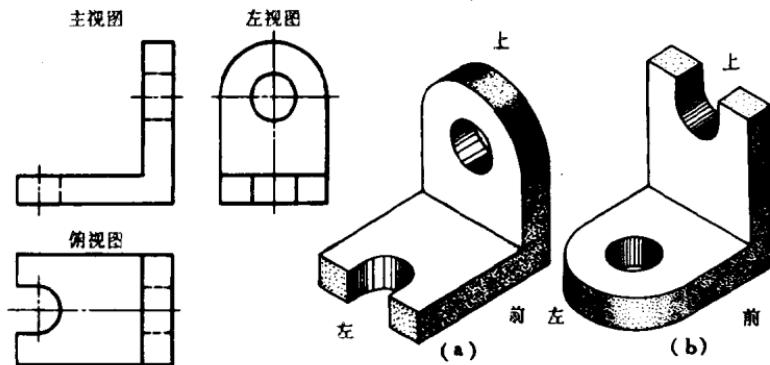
支架的三视图 图 1-16 根据视图特点, 摆正支架的位置
